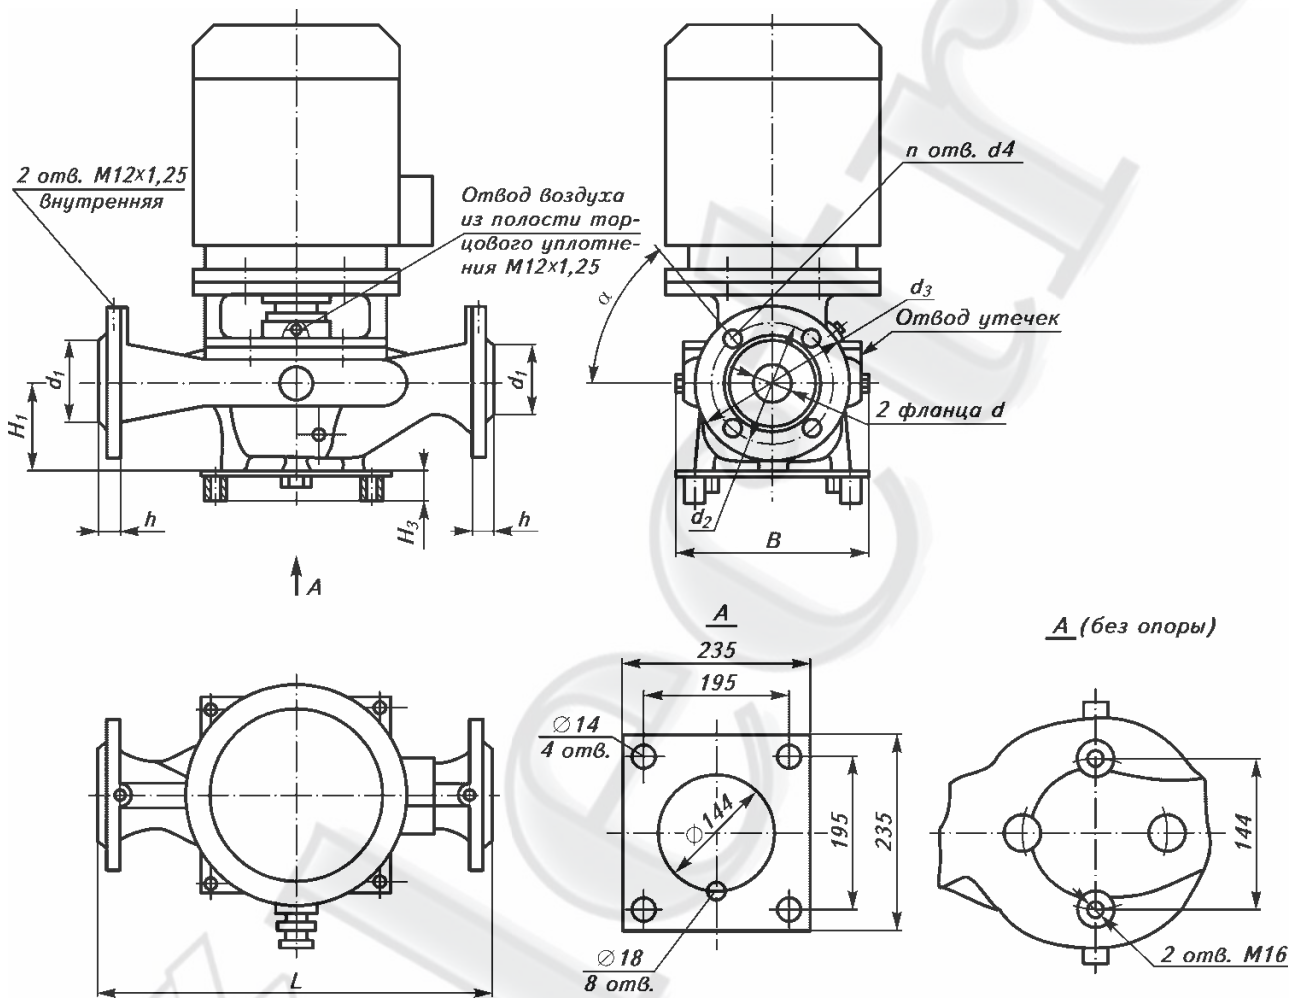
Общий вид, габаритные, присоединительные размеры и масса электронасосов типа КМЛ
